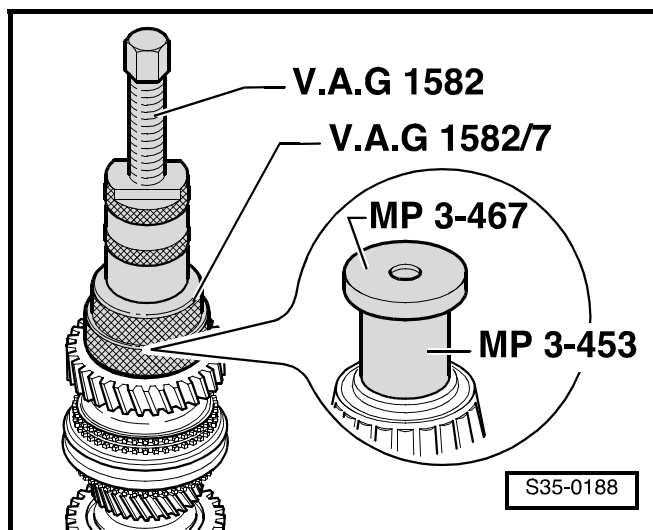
Выпрессовывание скользящей муфты и каретки синхронизатора для 5-ой и 6-ой передач с шестерней 6-ой передачи
